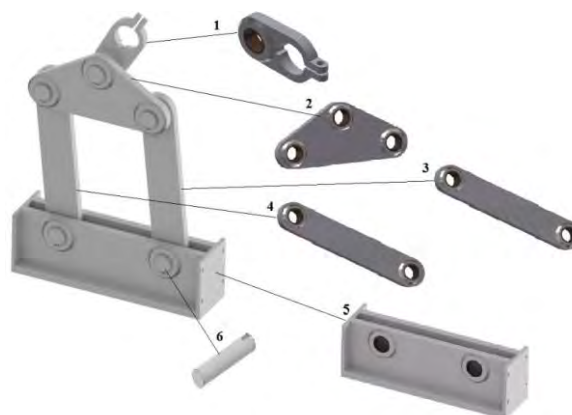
3-D модель плоского рычажного механизма 4-го класса: 1-кривошип, 2- трехпарное звено, 3,4 – шатуны, 5- ползун, 6 – соединительный палец.
